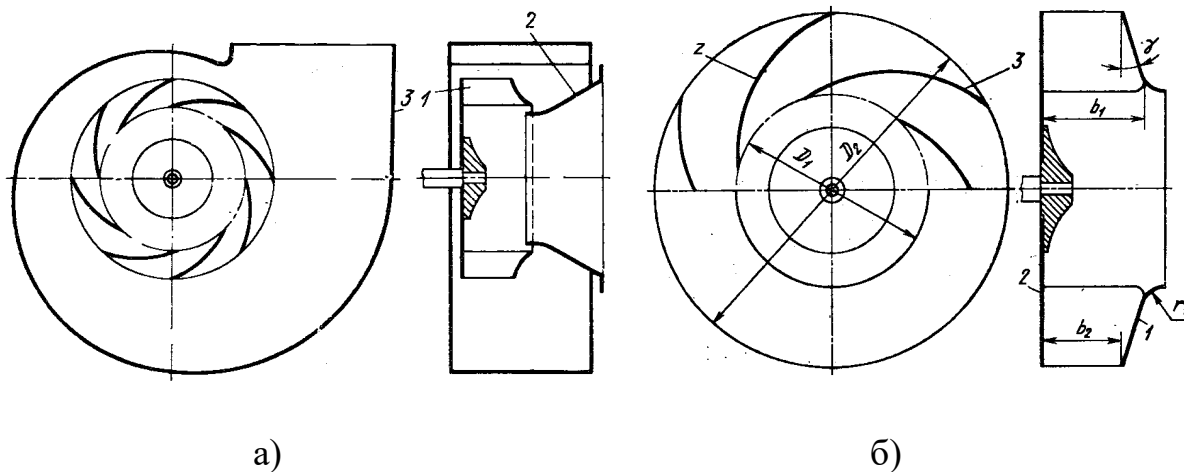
(а) — аэродинамическая схема центробежного вентилятора: 1 — рабочее колесо, 2 — входной патрубок, 3 — спиральный корпус; (б) — рабочее колесо: 1 — передний диск, 2 — задний диск, 3 — лопатки
